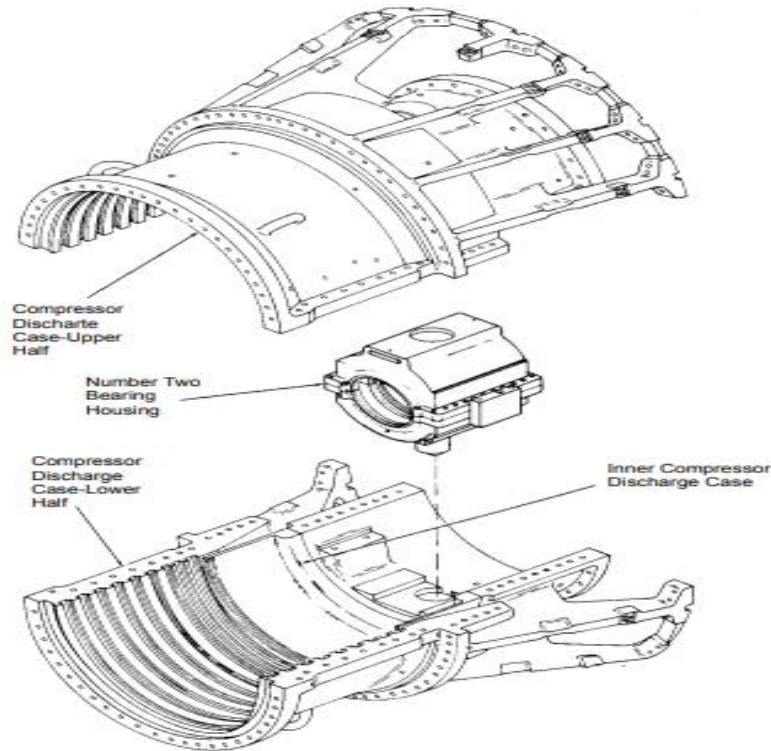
Assemblage du corps de compresseur, coté refoulement.
